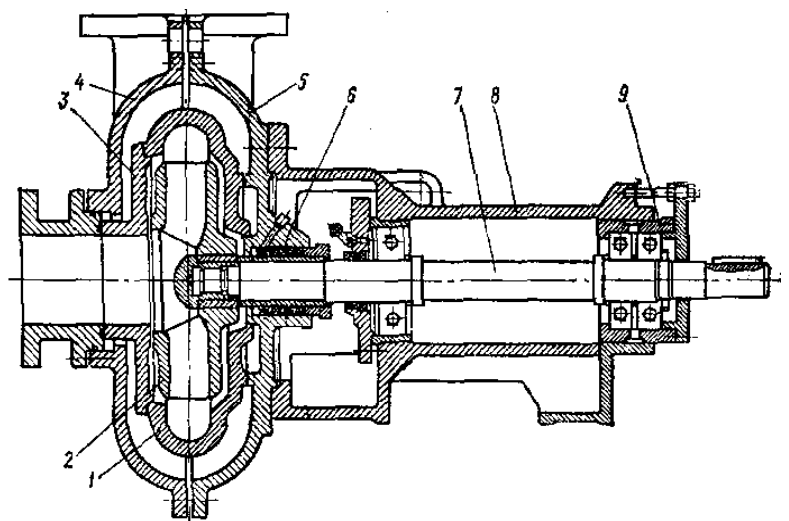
Двокорпусний ґрунтовий насос:
